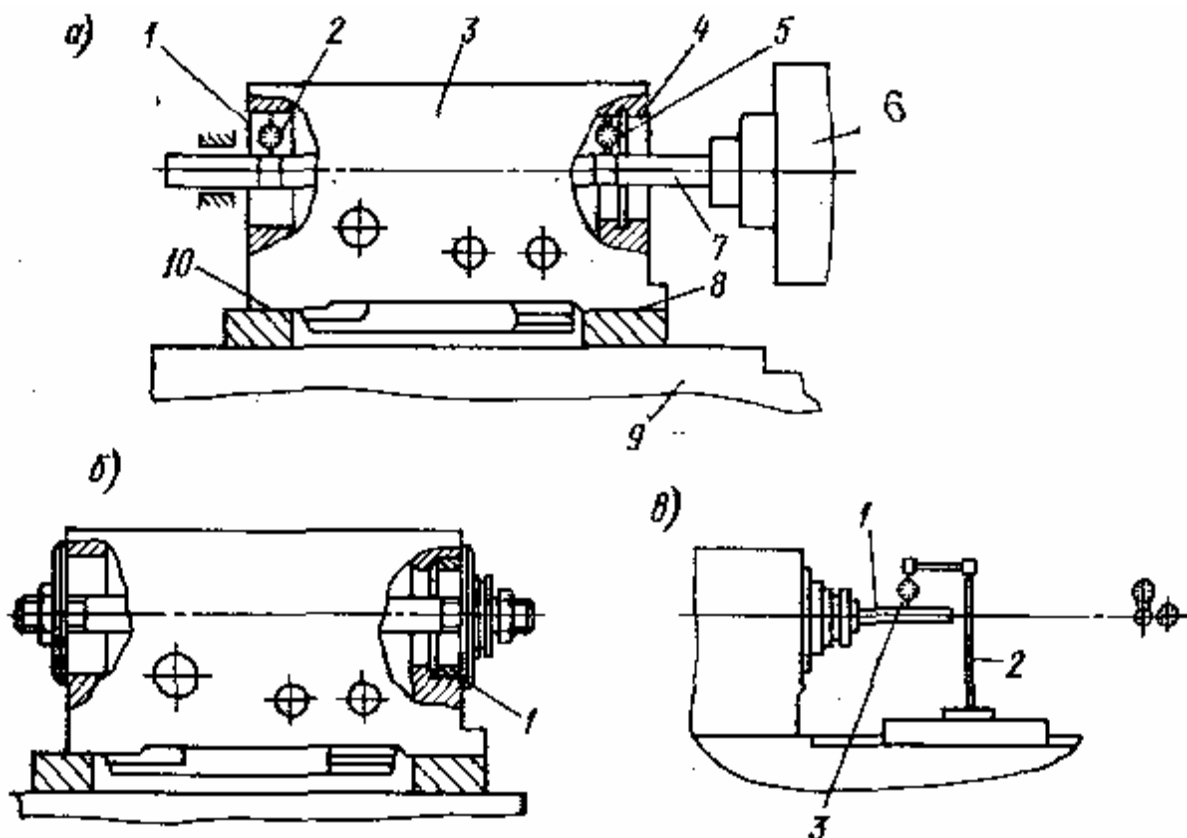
Схеми ремонту корпусу передньої бабки
